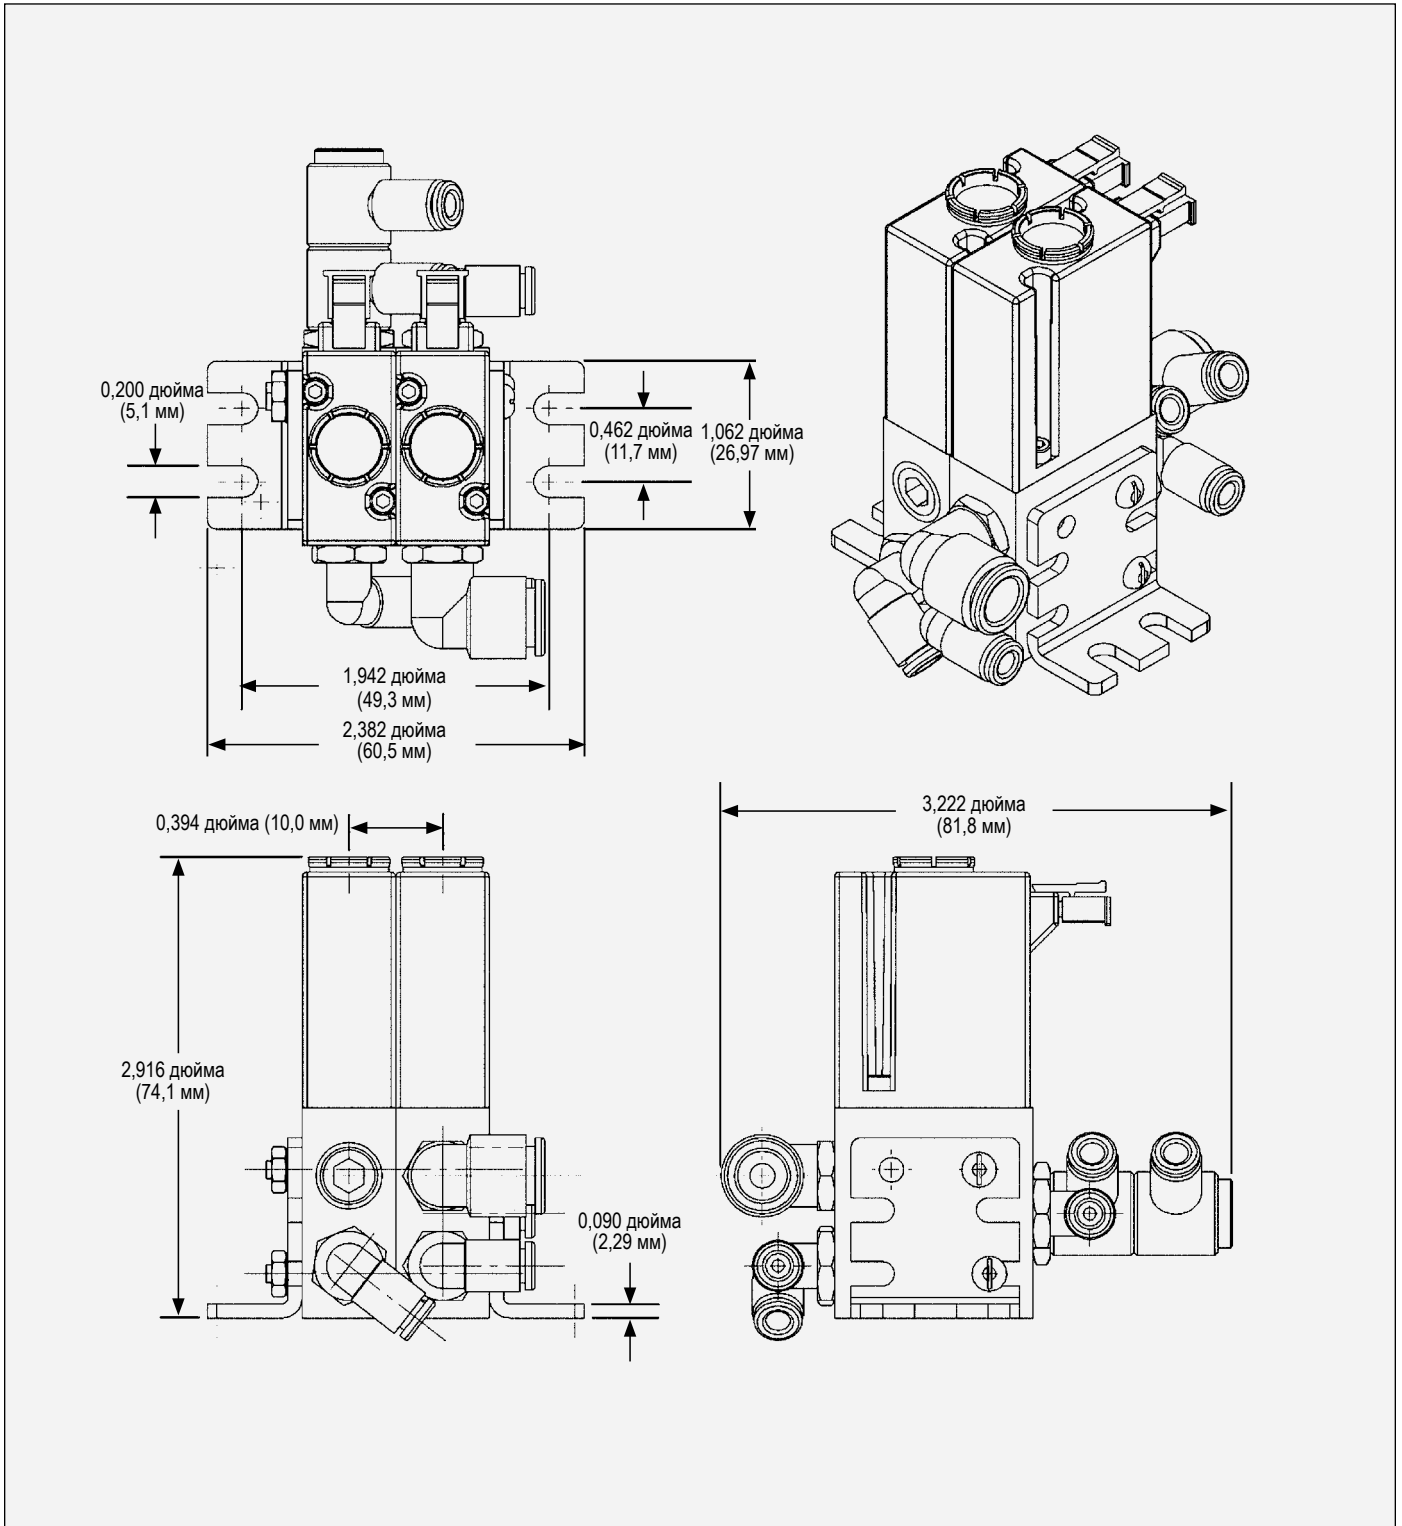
Размеры блока электромагнитных клапанов в сборе
